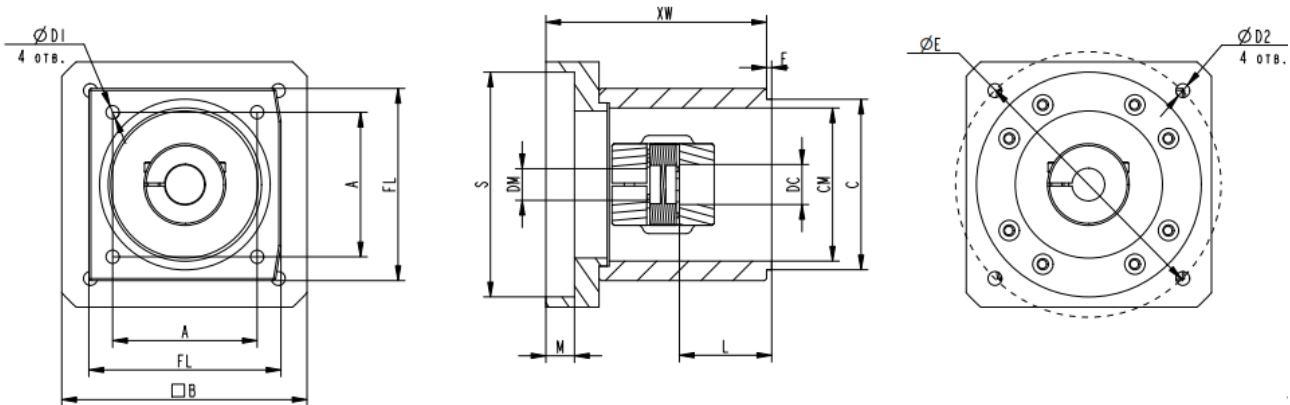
Набор для соосной установки двигателя и редуктора AP-MCR-112.
